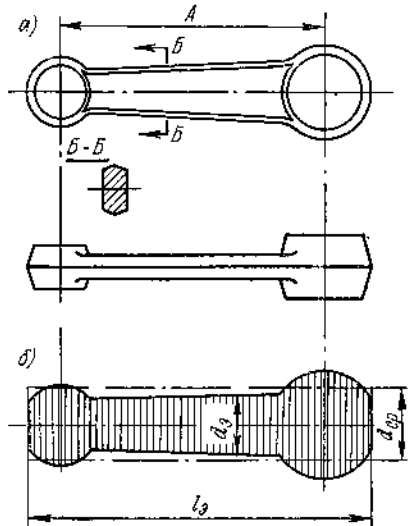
Чертеж поковки шатуна (а) и эпюра ее диаметров (б)
